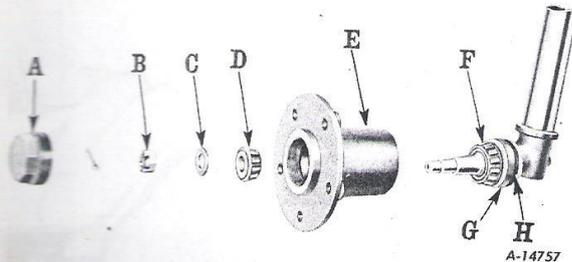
Moyeu et roulement de roue avant démontés pour le nettoyage.
